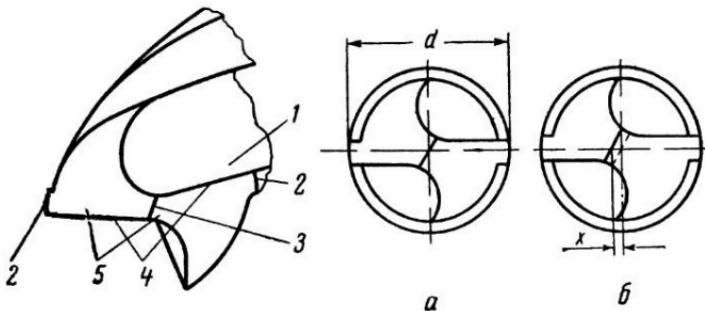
Режущая часть сверла. 1 — передняя поверхность; 2 — вспомогательные режущие кромки или ленточки; 3 — поперечная кромка (перемычка); 4 — главные режущие кромки; 5 — задние поверхности; *a* — перемычка расположена симметрично; *б* — перемычка смещена на величину *x*.
